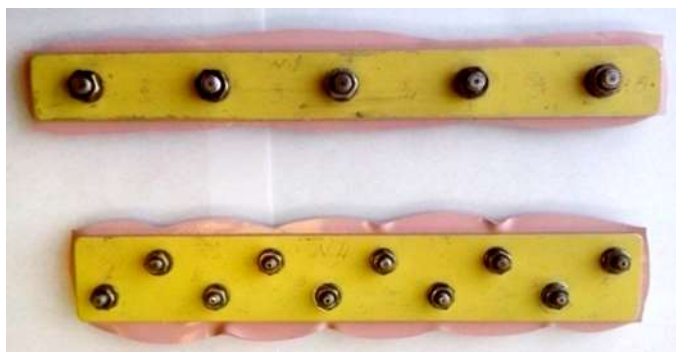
Образцы ленточного герметика с однорядными и двухрядными болтовыми соединениями
